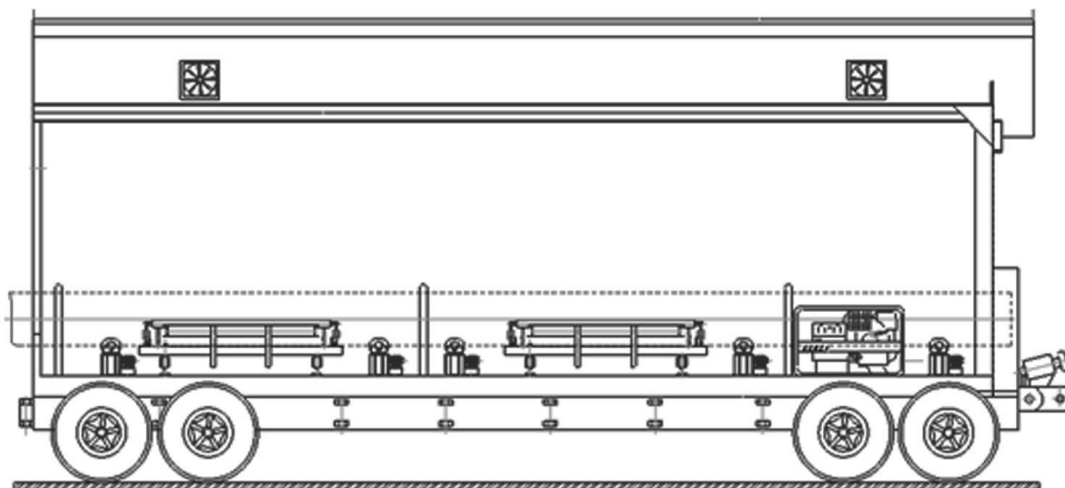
Платформа комплекса с устройствами подачи заготовок
